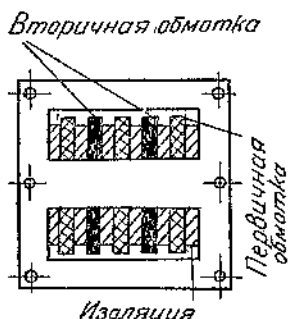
Цилиндрические обмотки сварочного трансформатора, расположенные на одном стержне.
